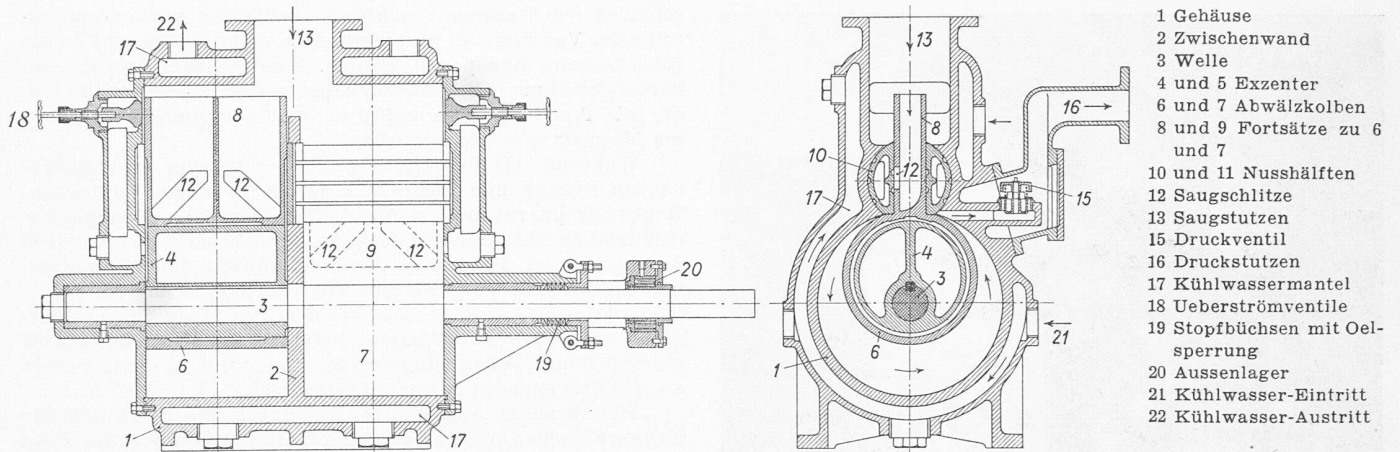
Vakuumpumpe mit Abwälzkolben, System Kinney
